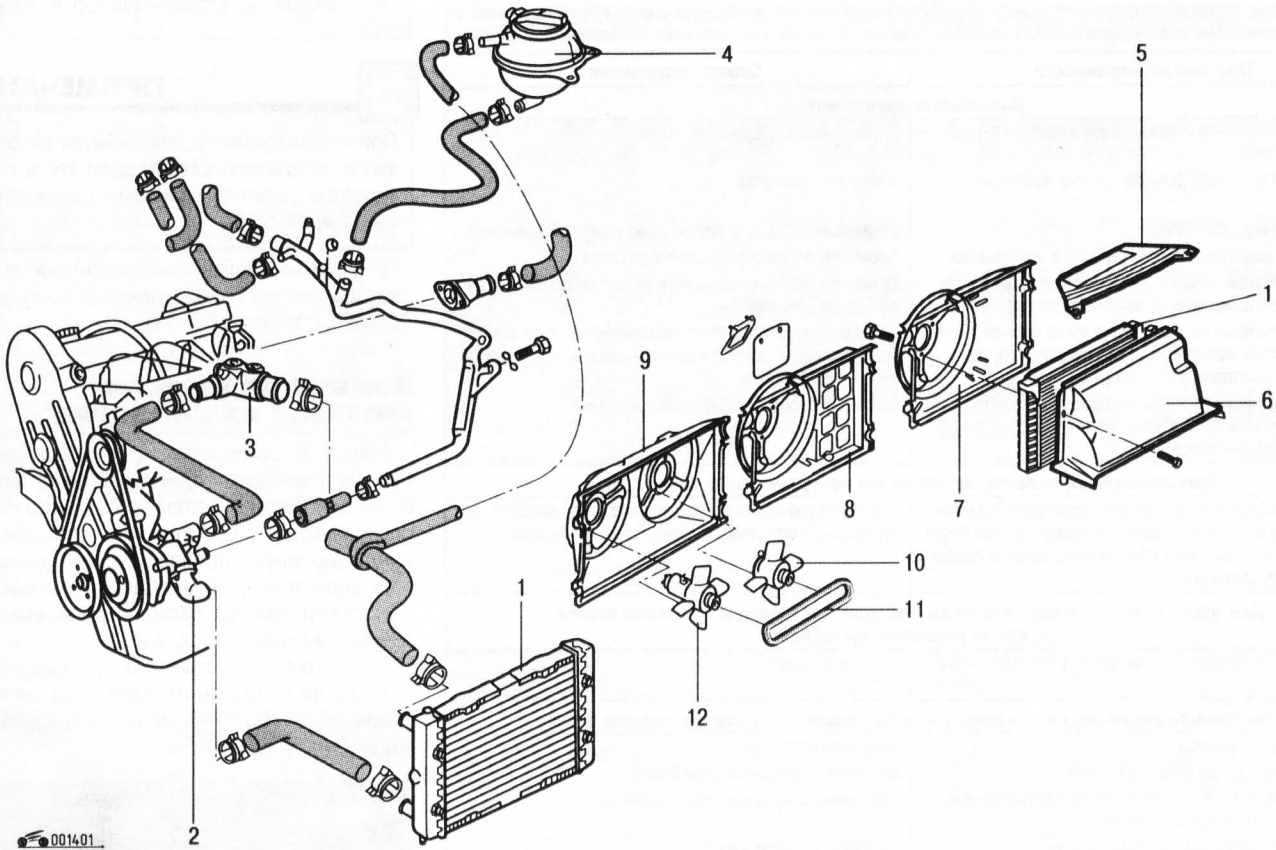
Система охлаждения двигателя SOHC: 1 – радиатор; 2 – водяной насос; 3 – соединительный патрубок; 4 – расширительный бачок; 5 – верхний защитный кожух; 6 – воздухонаправляющий кожух; 7 – кожух вентилятора (EZ); 8 – кожух вентилятора (PB, RP); 9 – кожух вентиляторов; 10 – дополнительный вентилятор; 11 – приводной ремень; 12 – электрический вентилятор
